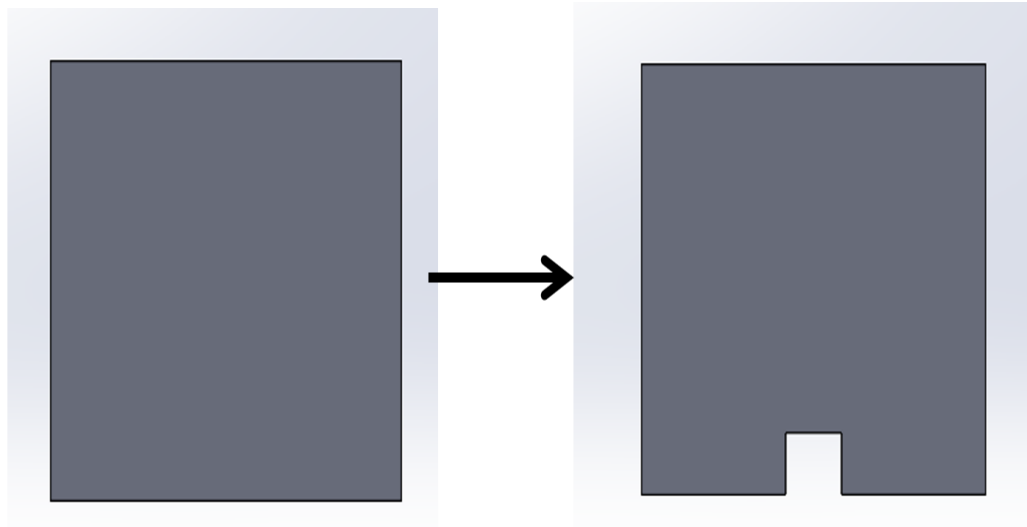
Cajeado para portillón en la chapa del portón.
